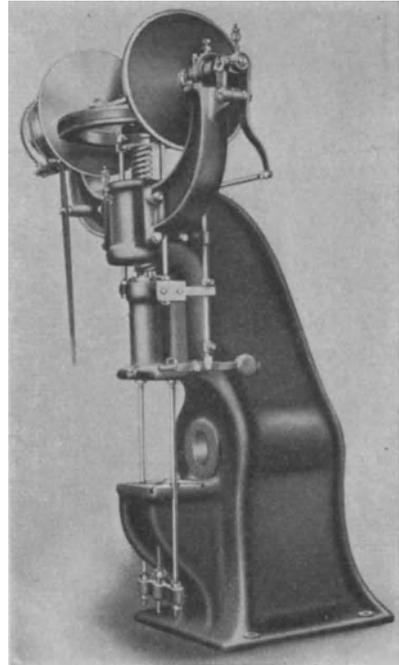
Friktionspresse mit offenem Maschinenkörper für Warmpreßteile.
